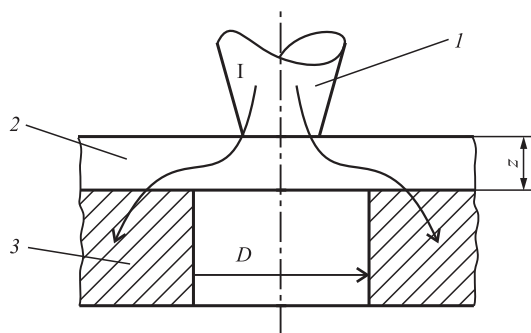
Схема нагрева листовой заготовки из титанового сплава импульсом электрического тока:
